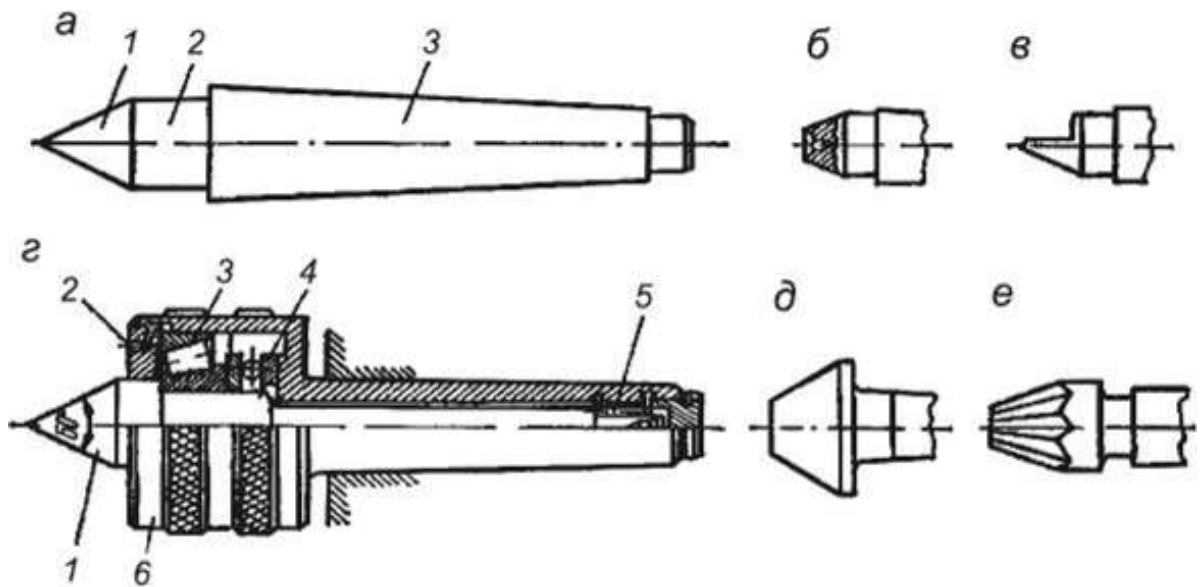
Види центрів: а – звичайний центр (1 центруючий конус, 2 – перехідна частина; 3 – конус Морзе); б – зворотний центр; в – скошений центр; г - задній центр, що обертається (1 - центруючий конус, 2 - фіксатор; 3 - радіально упорний підшипник; 4 - упорний підшипник; 5 - корпус з конусом Морзе, 6 - кришка); д-грибковий конус; е – рифлений центр.
